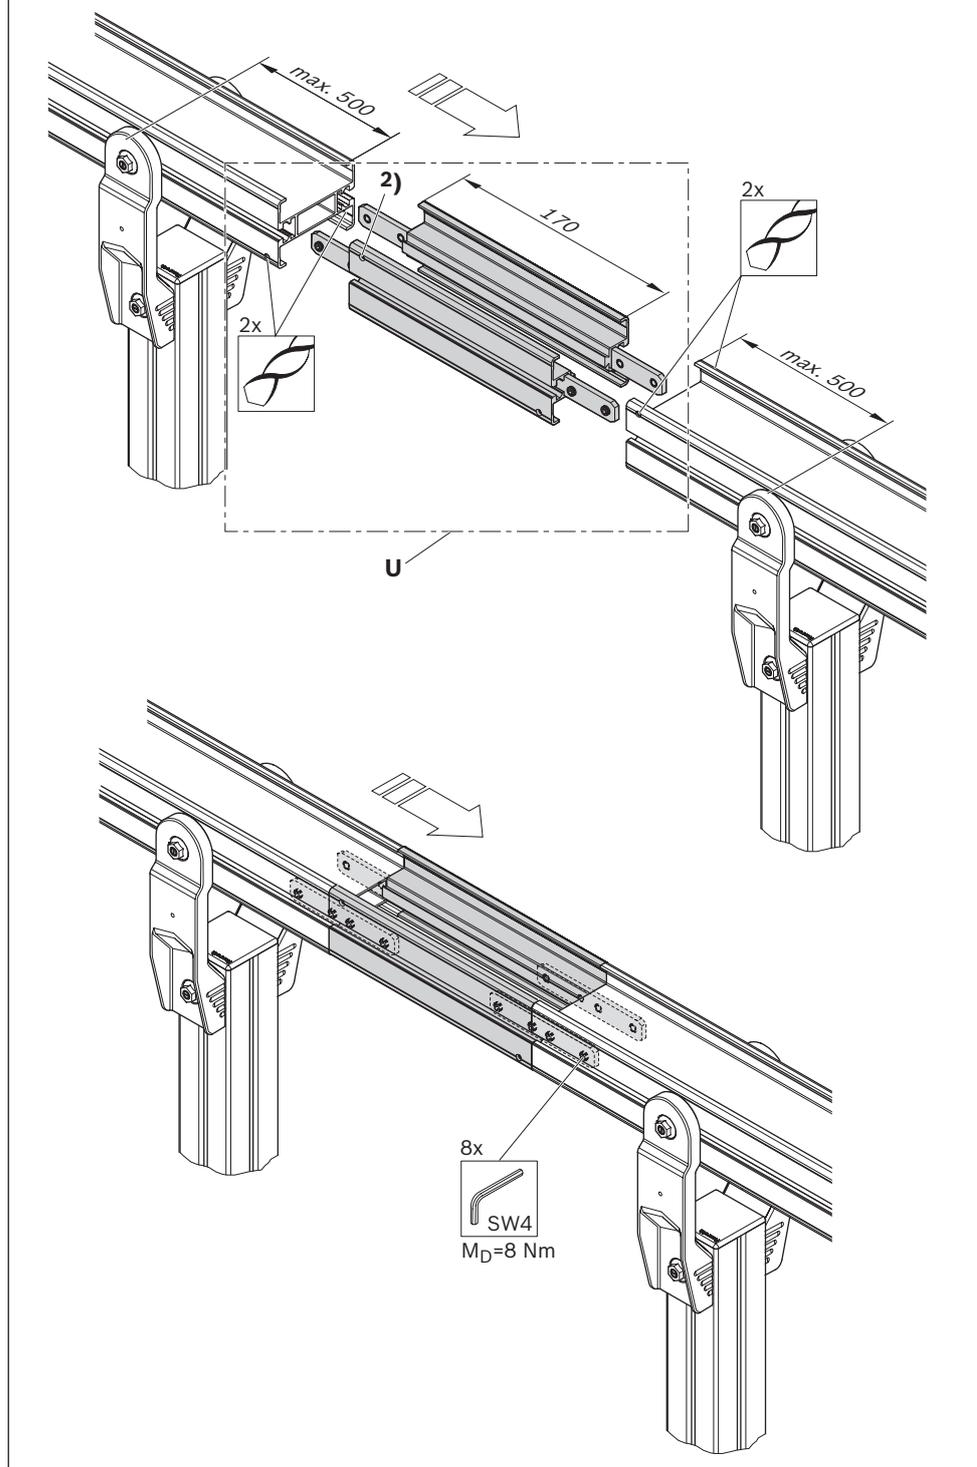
Sistema AL, montaggio del modulo di montaggio
